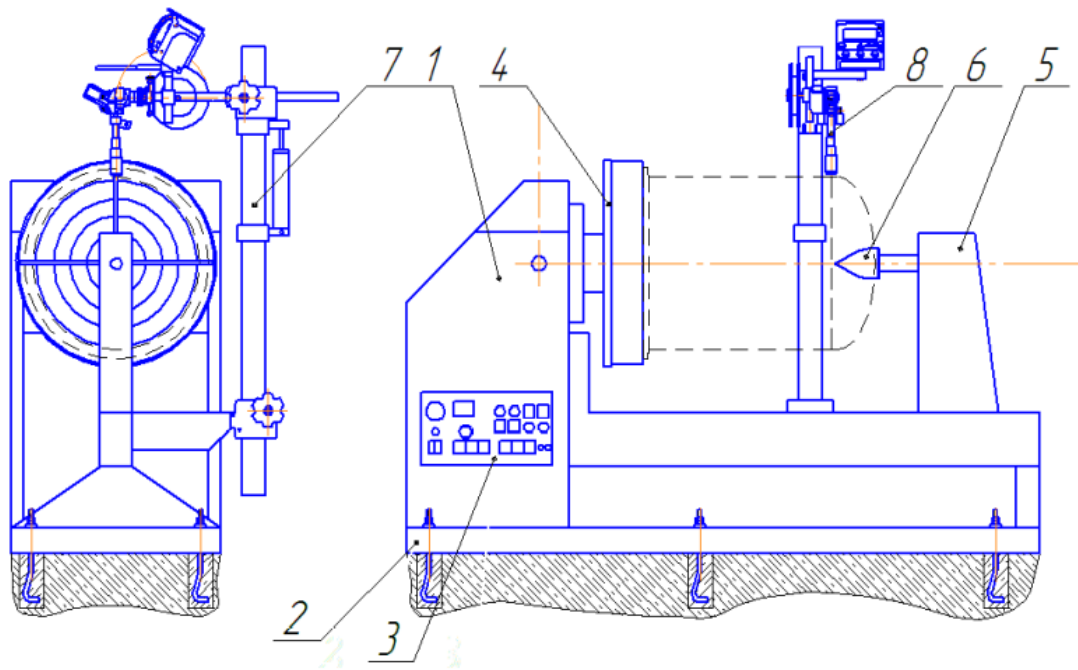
Обертач для автоматичного зварювання TRAV 600 BACB: 1 – станина з обертовим механізмом; 2 – опорна плита; 3 – блок керування; 4 – планшайба; 5 – задня бабка; 6 – самоцентруючий механізм; 7 – пневматична консоль; 8 – зварювальна головка Мультитрак А2 (GMAW).
